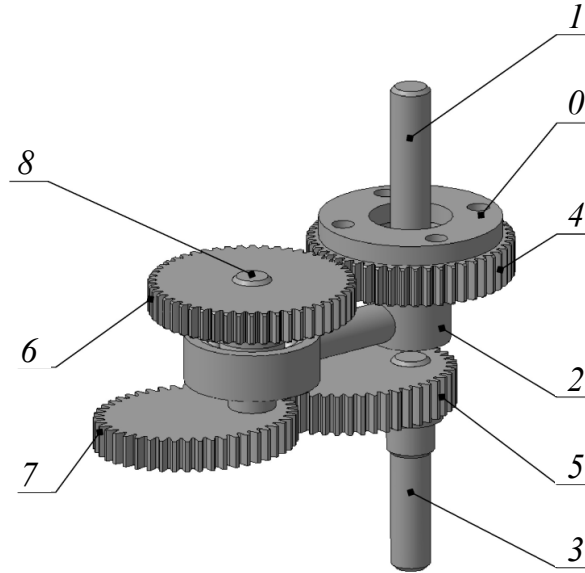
Планетарный приводной механизм перемешивающего устройства
